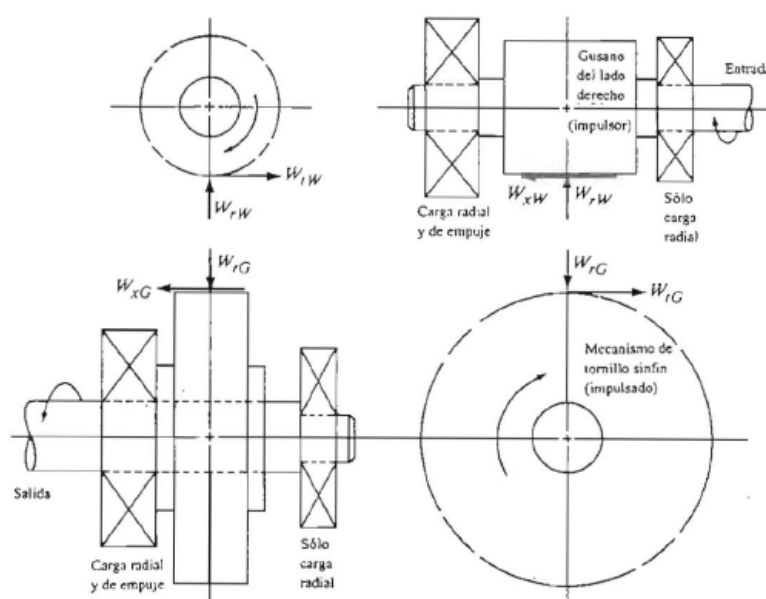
FUERZAS EN UN GUSANO Y EN UN MECANISMO DE TORNILLO SIN FÍN
